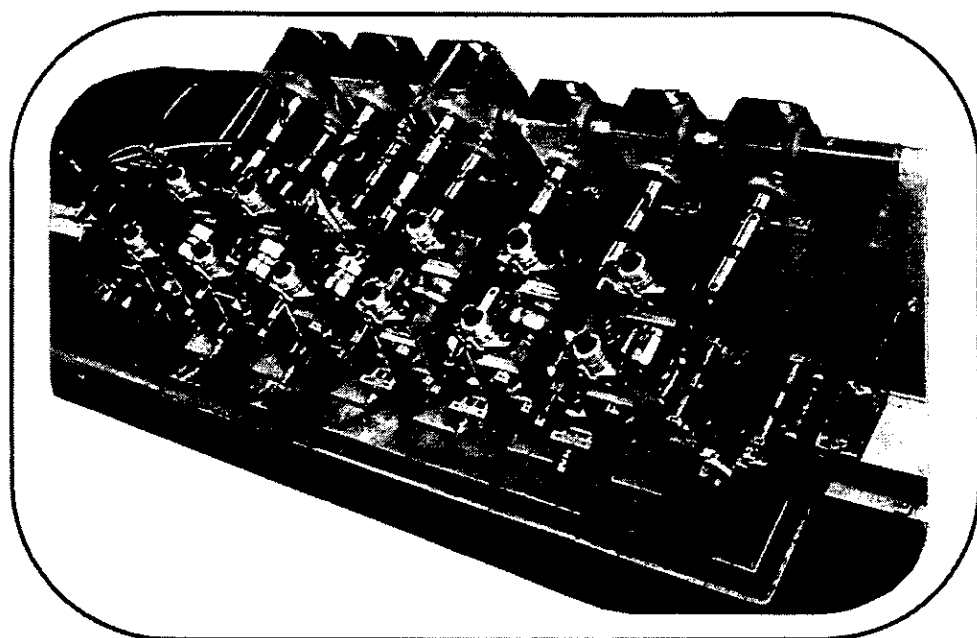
Equipo para la fabricación de tubo soldado de la marca T&H Machine Inc.(4)
